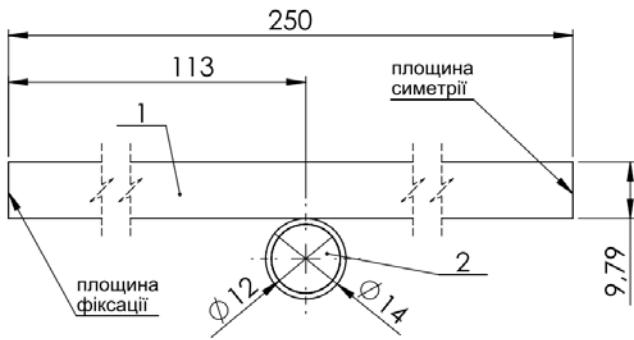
Схема реалізації віброударного режиму: 1 – плоска пружина; 2 – полімерно-металева циліндрична опора
